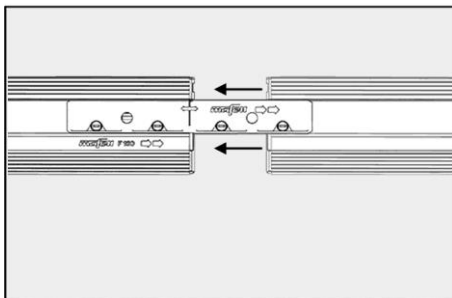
Соединительный элемент F-VS для соединения двух направляющих шин
